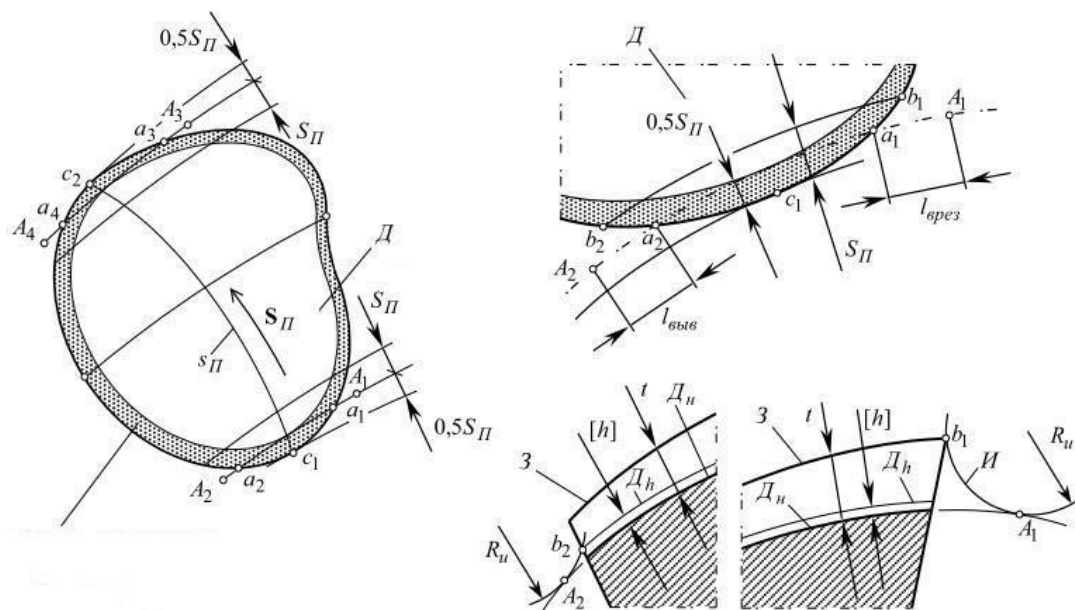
Визначення положення точки початку обробки складної поверхні деталі на багатокоординатному верстаті з ЧПК
